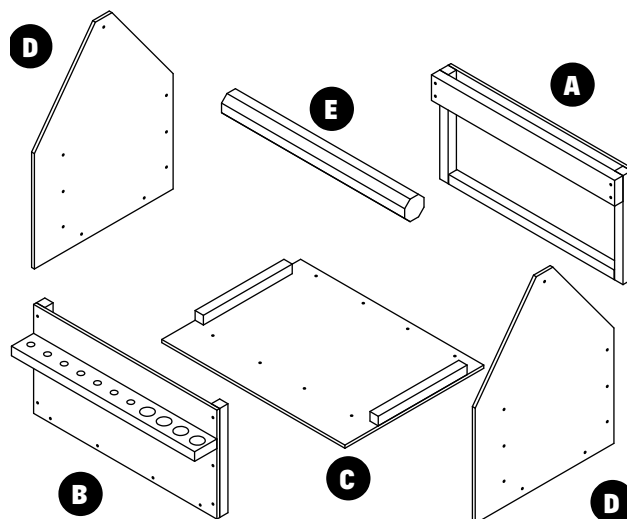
Vue éclatée et numérotation des sous-ensembles
